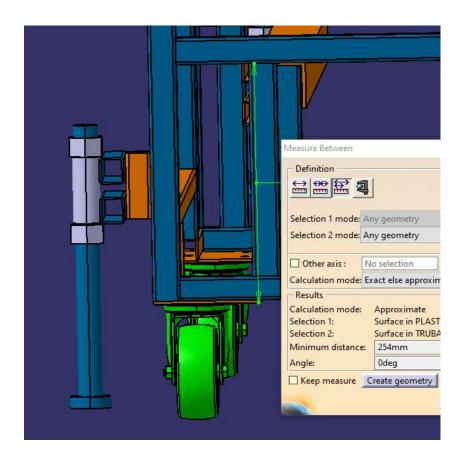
Высота между плитой для колес и трубой закрепления AGV с рамой
